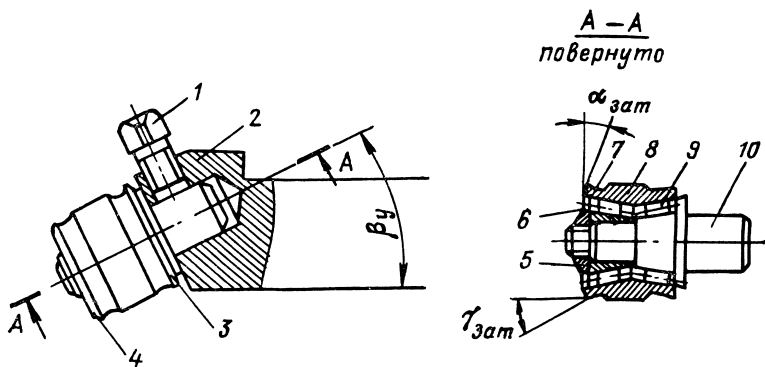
Резец для ротационного резания на подшипниках качения: 1 — болт; 2 — державка; 3, 4 — круговые режущие кромки; 5 — гайка; 6 — защитная шайба; 7 — режущий нож; 8 — подшипники радиально-упорные; 9 — тела качения; 10 — ось валика
